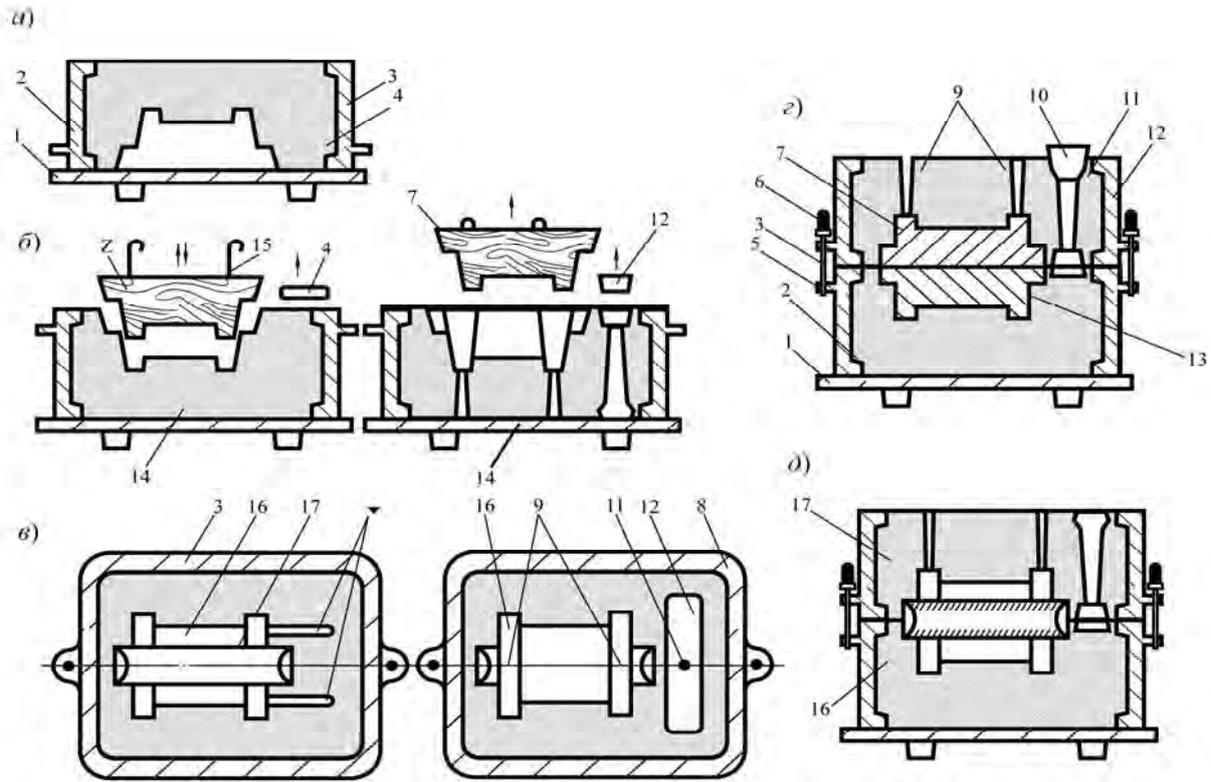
Последовательность процесса изготовления сырой песчано-глинистой формы ручным способом
